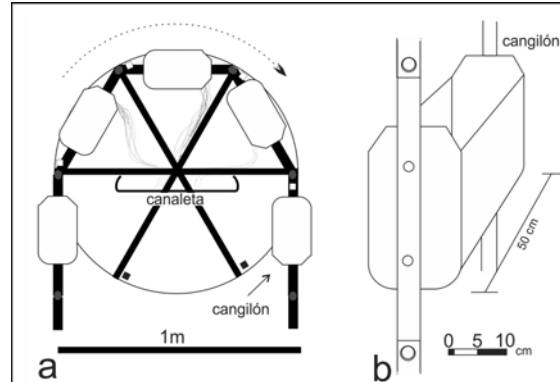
a, Vista corte longitudinal de la cadena de cangilones; b, Esquema de un cangilón con su eslabón.
